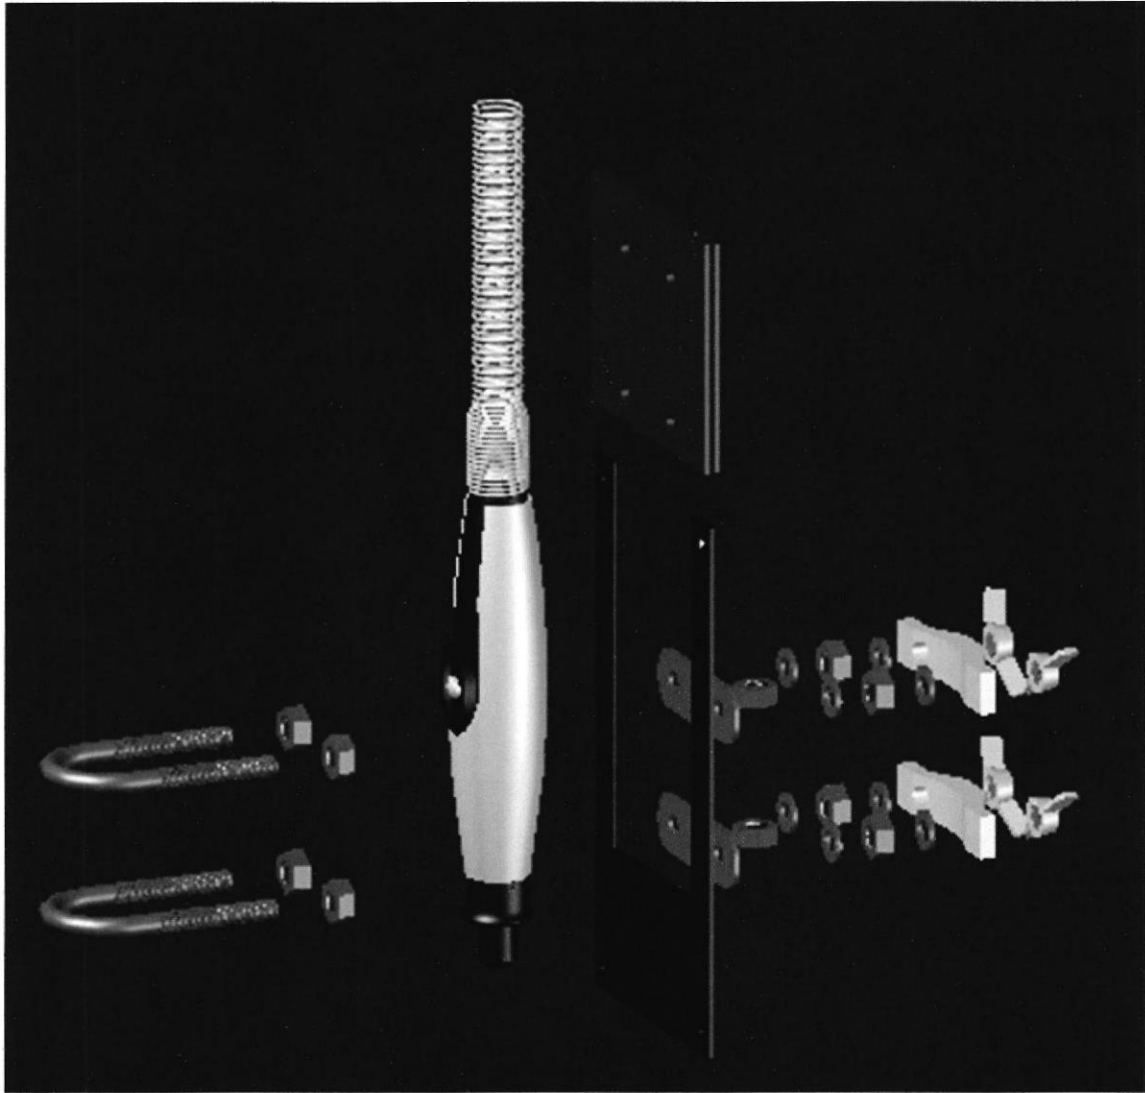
Vista de la pieza doble que sujeta al eje flexible, y del conjunto de materiales para sujeción.
